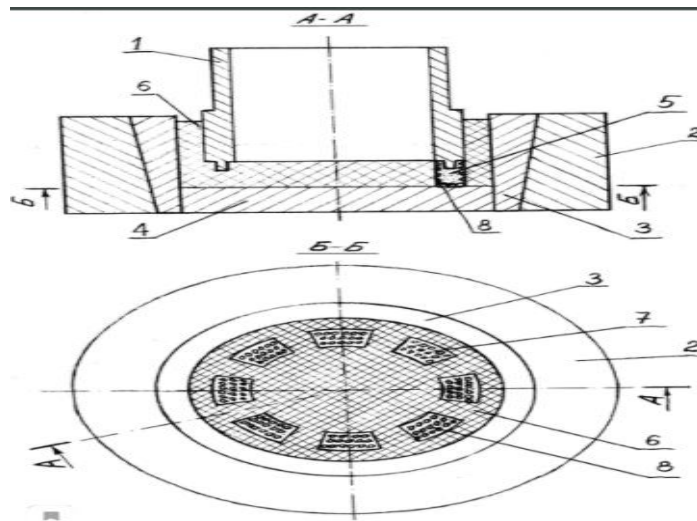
Пресс-форма с установленным корпусом в двух проекциях (вид сбоку и снизу) [3.6]
